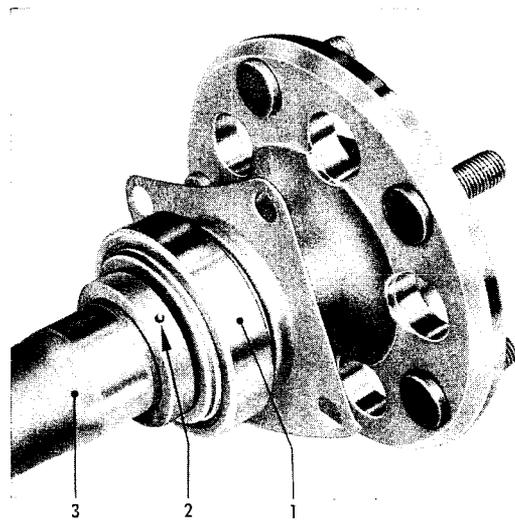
Haltering für Kugellager zum Bohren gekörnt
